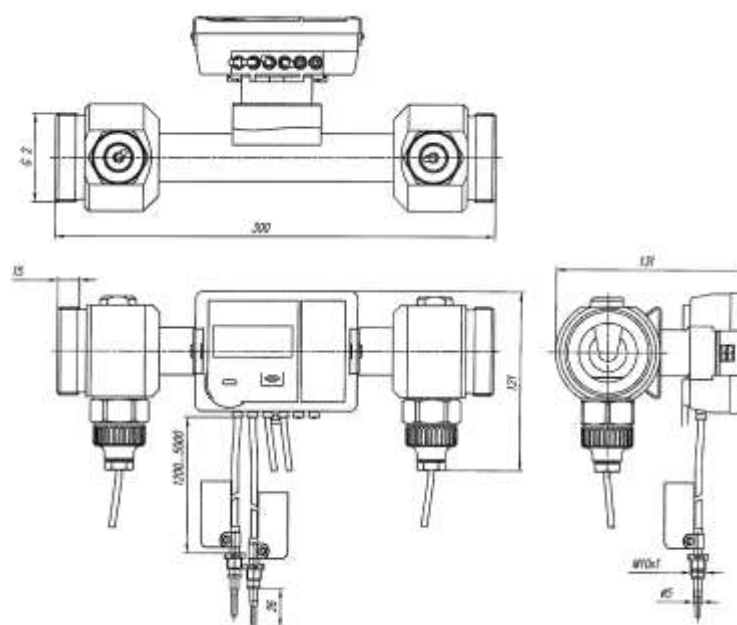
Присоединительный размер к трубопроводу G2" , длина L=300 мм
